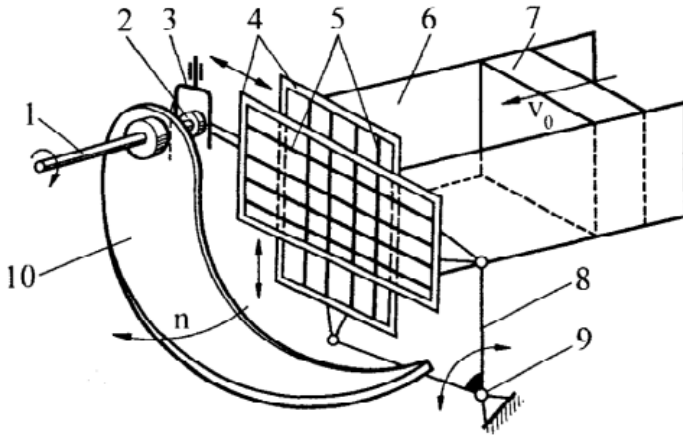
Принципова схема ріжучого вузла шпигоріза: 1 - приводний вал; 2 - ексцентрик; 3 - вилка; 4 - ножові рамки; 5 - пластинчасті ножі; 6 - короб живильника; 7 - штовхач; 8 - кутовий важіль; 9 - шарнір; 10 - серповидний ніж.
